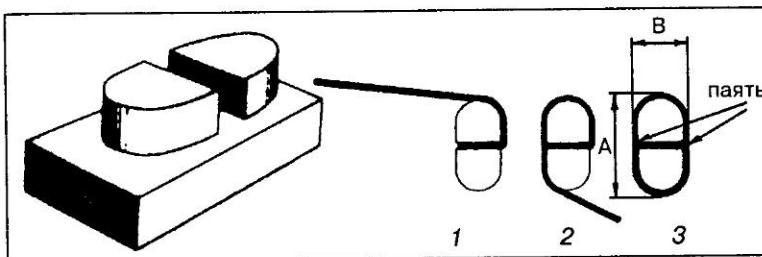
Гибочное приспособление для изготовления звеньев якорной цепи
